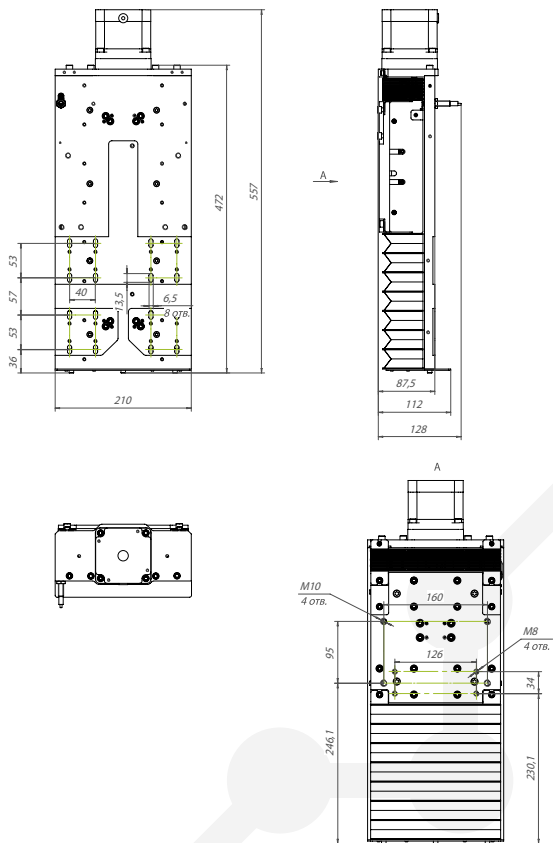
Габаритный чертеж модуля оси Z RY-Z170-RM16
